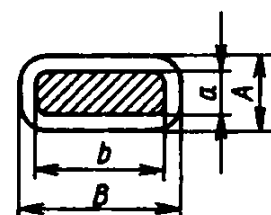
Схема обмоточного провода прямоугольного сечения
